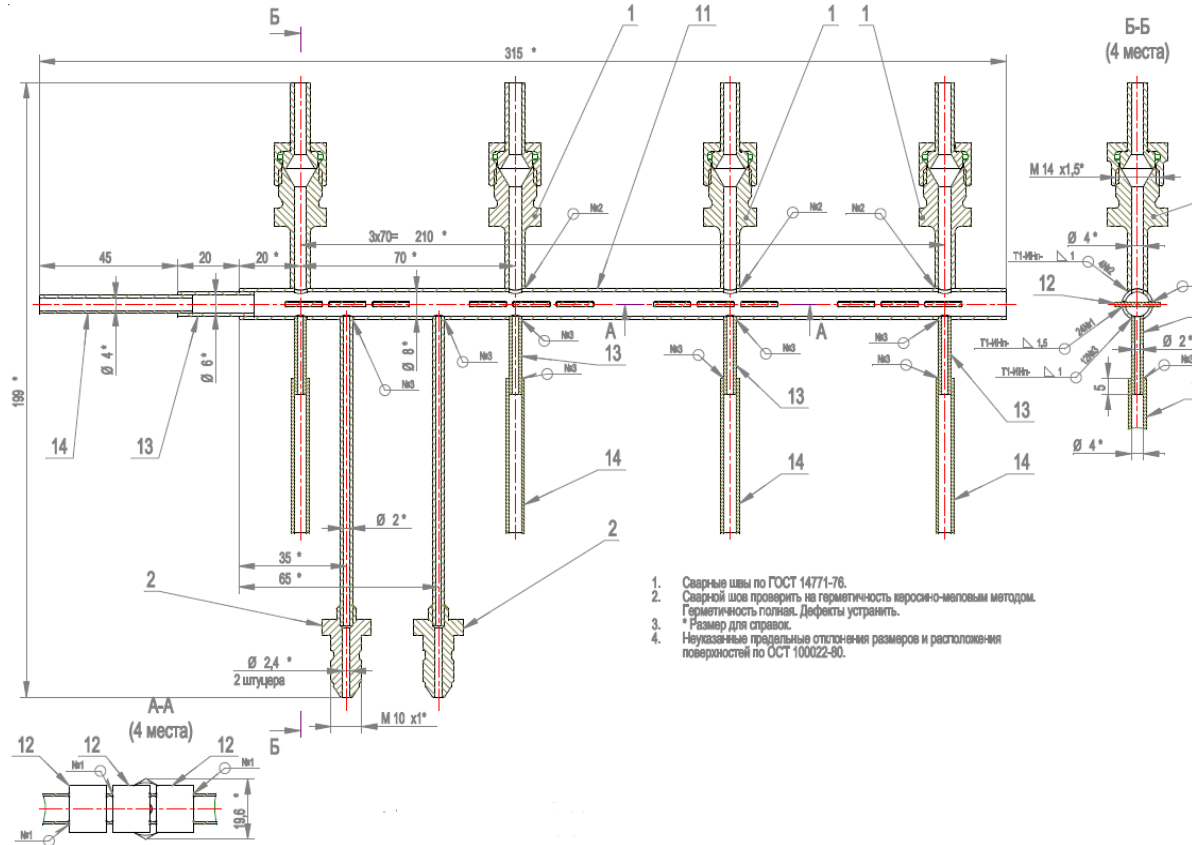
Фрагмент сборочного чертежа трубка с профилями
